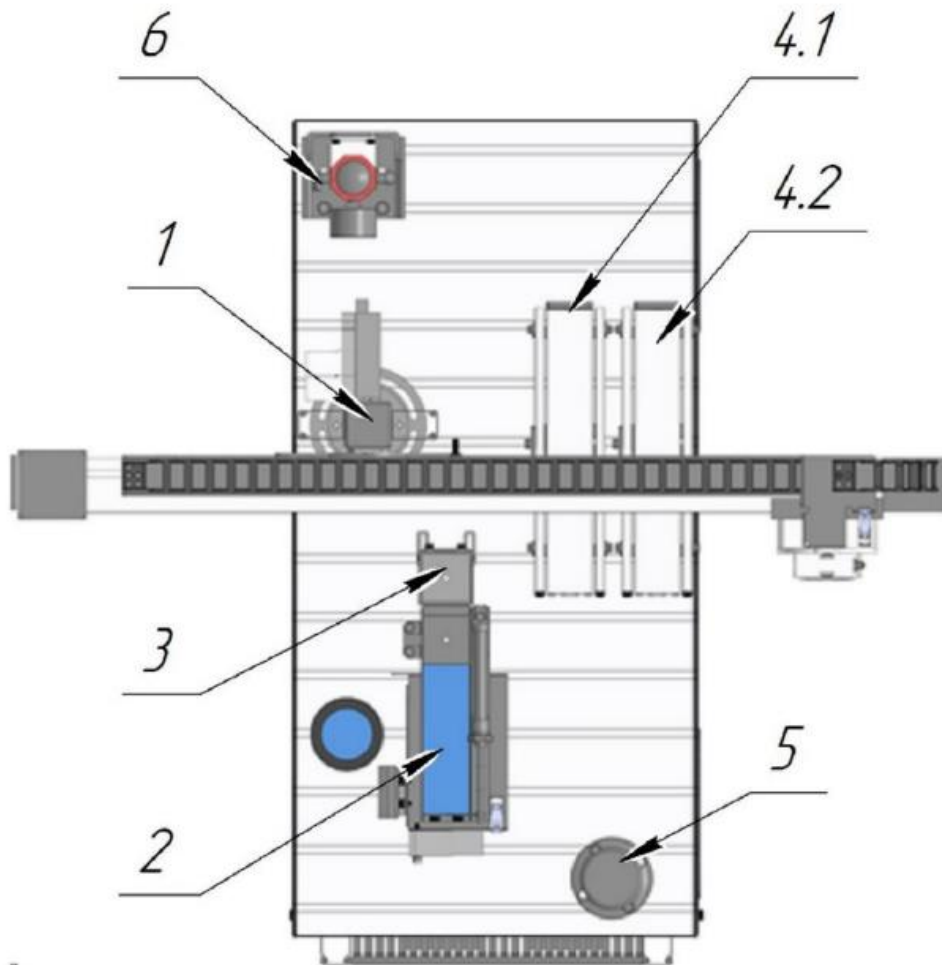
Конструкция мехатронной станции (вид сверху):
